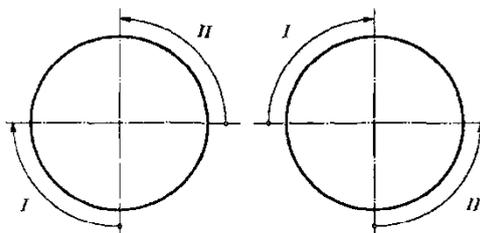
Порядок наложения корневого слоя шва при сварке вертикального неповоротного стыка двумя сварщиками
